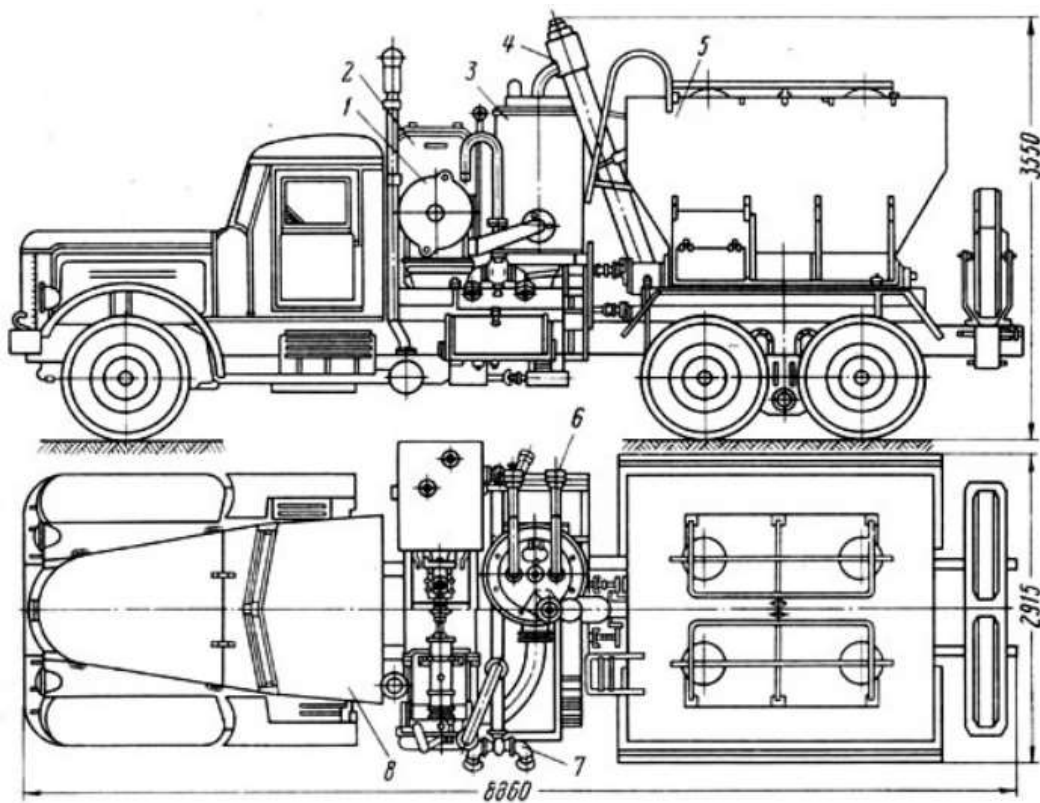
Піскозмішувальний агрегат ЗПА:
